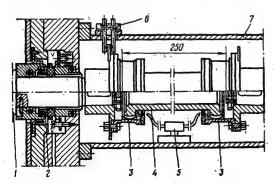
Зубчатая муфта, соединяющая валы компрессора и мультипликатора:
